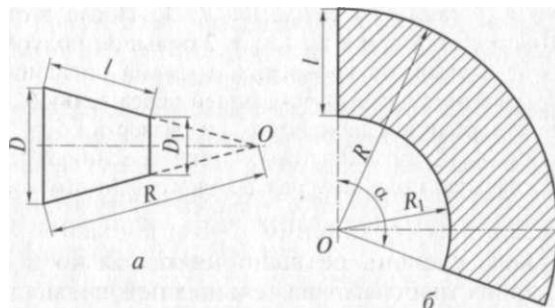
Построение развѣтки сварного концентрического перехода:
